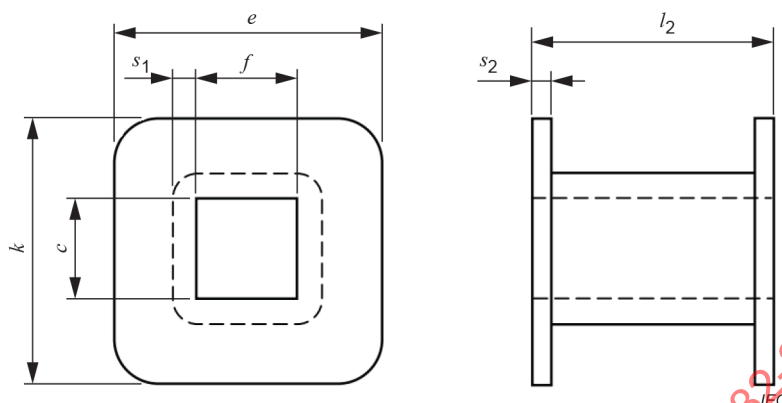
Dimensions principales des supports de bobinages pour noyaux E
